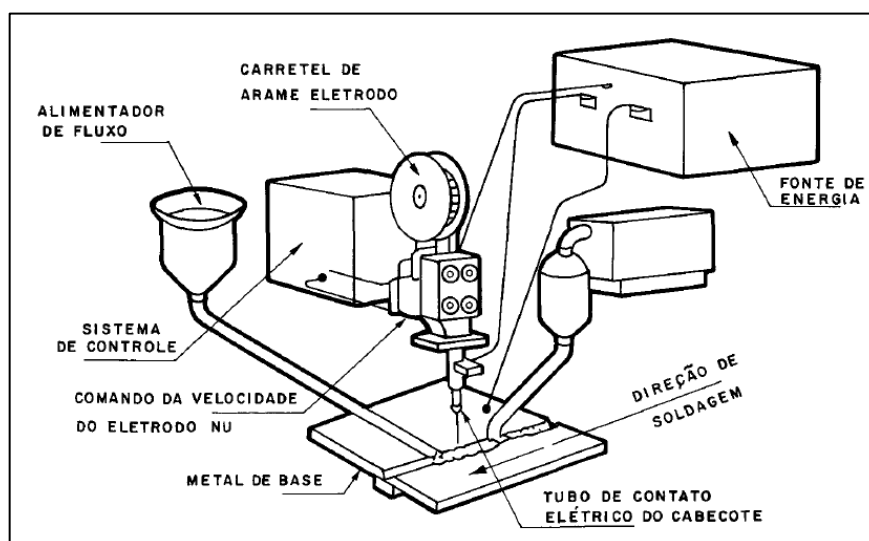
Exemplo de processo de soldagem por arco submerso (SAW) (12)
